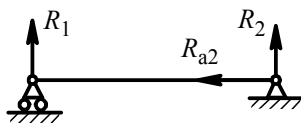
Схема установки вала на одной плавающей и одной фиксирующей опоре с одним подшипником в ней
